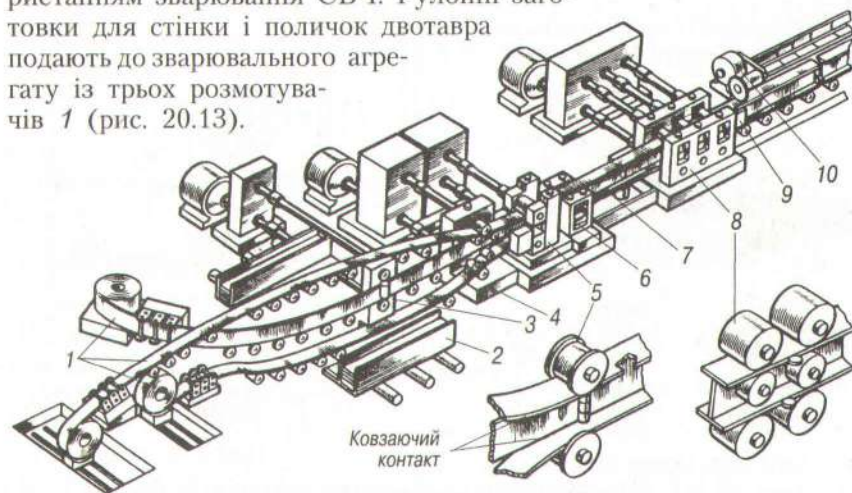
Схема агрегату для виготовлення двотаврових профілів зварюванням СВЧ:
